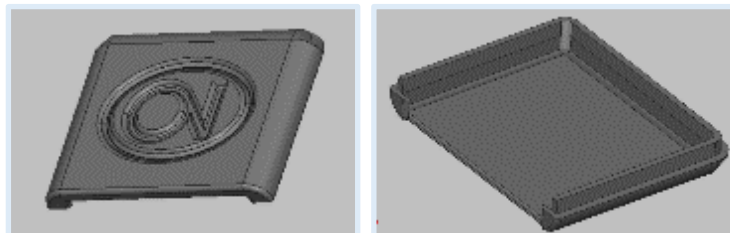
Diseño CAD 3D de envolvente para placa electrónica WRIST del demostrador SMART ARM
